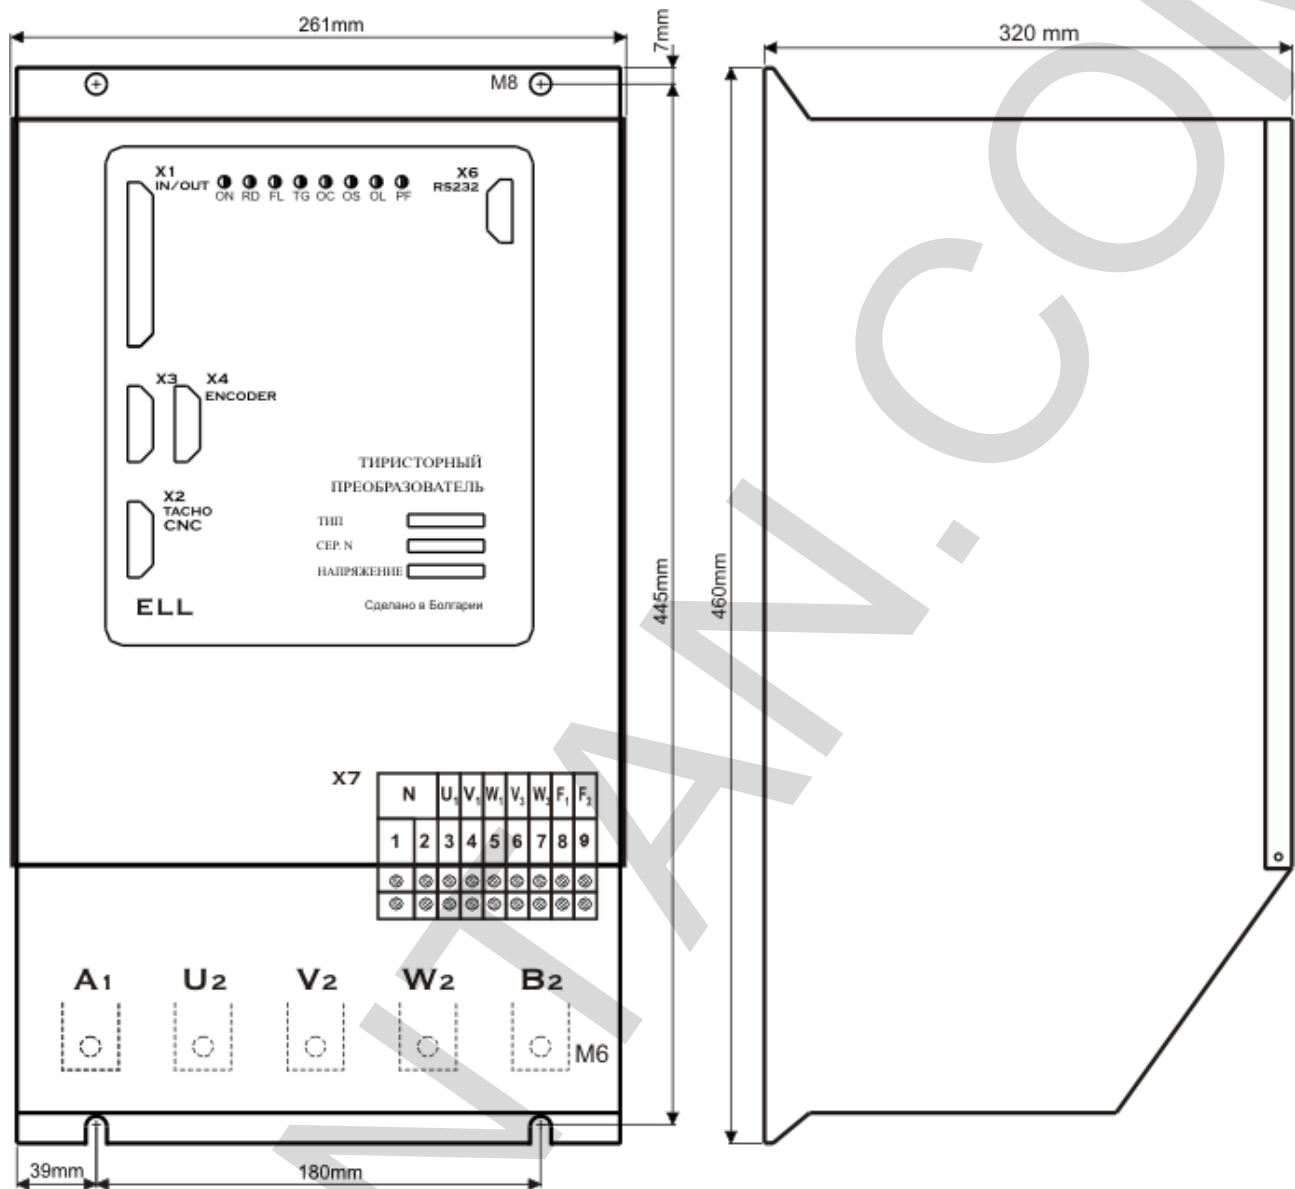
Присоединительные и габаритные размеры преобразователей 4002, 4003, 4004 и 4005
